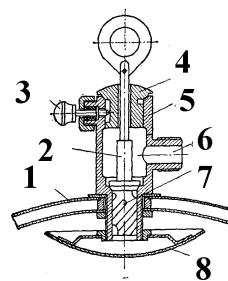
Клапан-турбінка: 1 – кришка котла; 2 – шпиндель з кільцем; 3 – фіксатор; 4 – обмежувач; 5 – корпус; 6 – штуцер для приєднання до паровідводу; 7 – клапан (турбінка); 8 – відбивач
